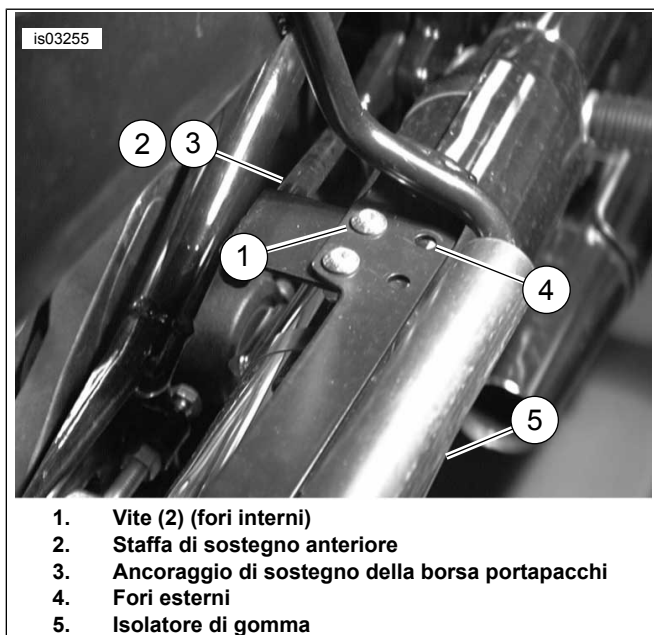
Installazione dell'indicatore di direzione e la staffa di riposizionamento
